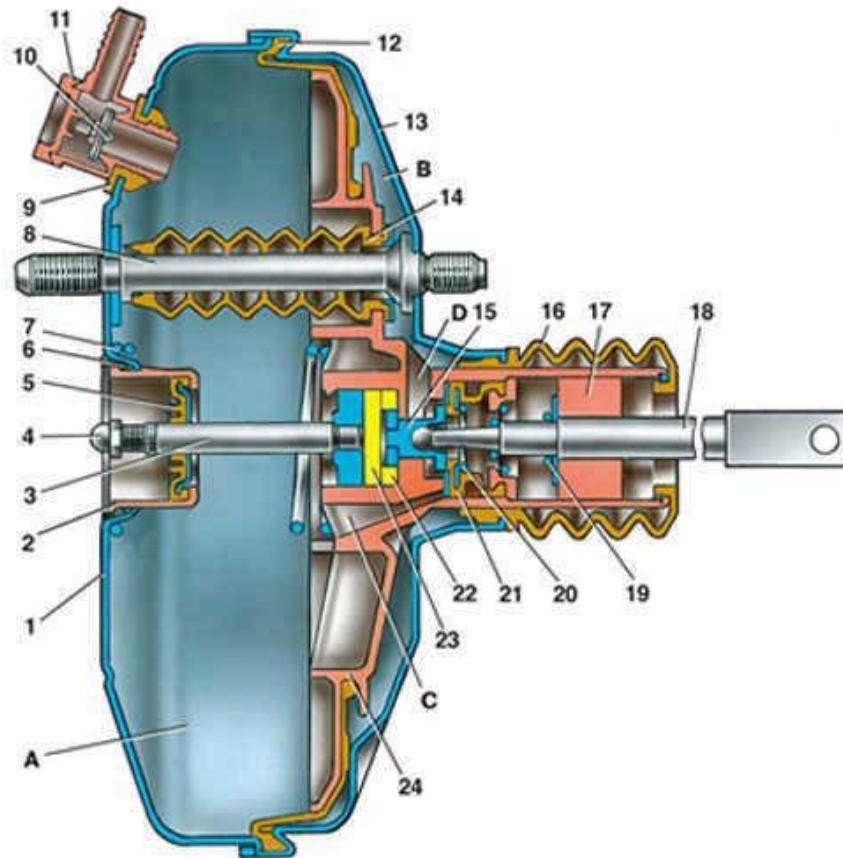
Вакуумний підсилювач гальм автомобіля ВАЗ 2110: 1 – корпус вакуумного підсилювача; 2 – чашка корпуса підсилювача; 3 – шток; 4 – регулювальний болт; 5 – ущільнювач штока; 6 – ущільнювальне кільце фланця головного циліндра; 7 – зворотна пружина діафрагми; 8 – шпилька підсилювача; 9 – фланець кріплення наконечника; 10 – клапан; 11 – наконечник шланга; 12 – діафрагма; 13 – кришка корпуса підсилювача; 14 – ущільнювальний чохол; 15 – поршень; 16 – захисний чохол корпуса клапана; 17 – повітряний фільтр; 18 – штовхач; 19 – зворотна пружина штовхача; 20 – пружина клапана; 21 – клапан; 22 – втулка корпуса клапана; 23 – буфер штока; 24 – корпус клапана; А – вакуумна камера; В – атмосферна камера; С, D – канали.
